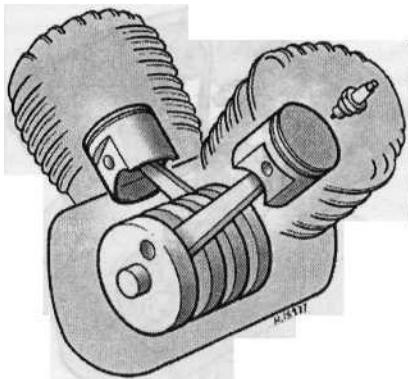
г Двухтактный V-образный двухцилиндровый двигатель
